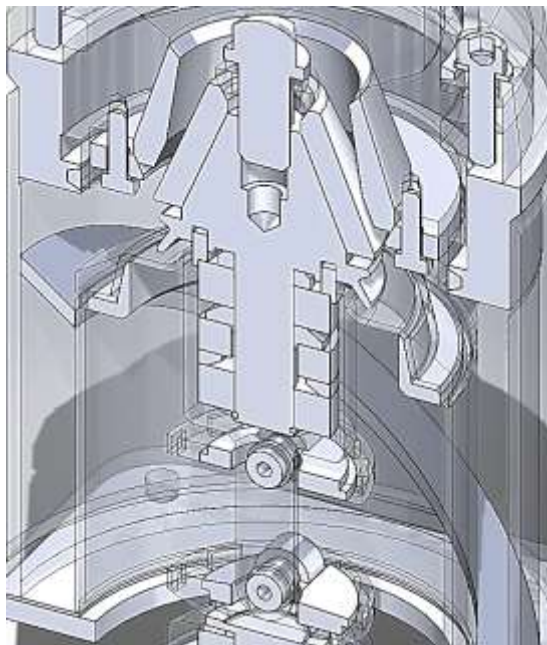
Модель конусной дробилки с усовершенствованной конструкцией эксцентрикового узла
